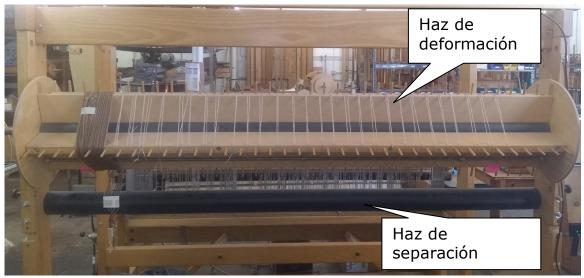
Viga de urdimbre y viga de separación en telar de madera
